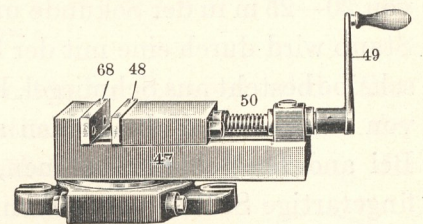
Drehbarer Schraubstock der Universalfräsmaschine.
